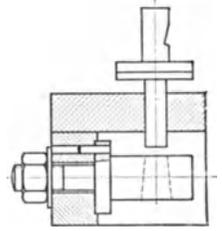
Befestigung einer hornförmigen Schnittplatte.
